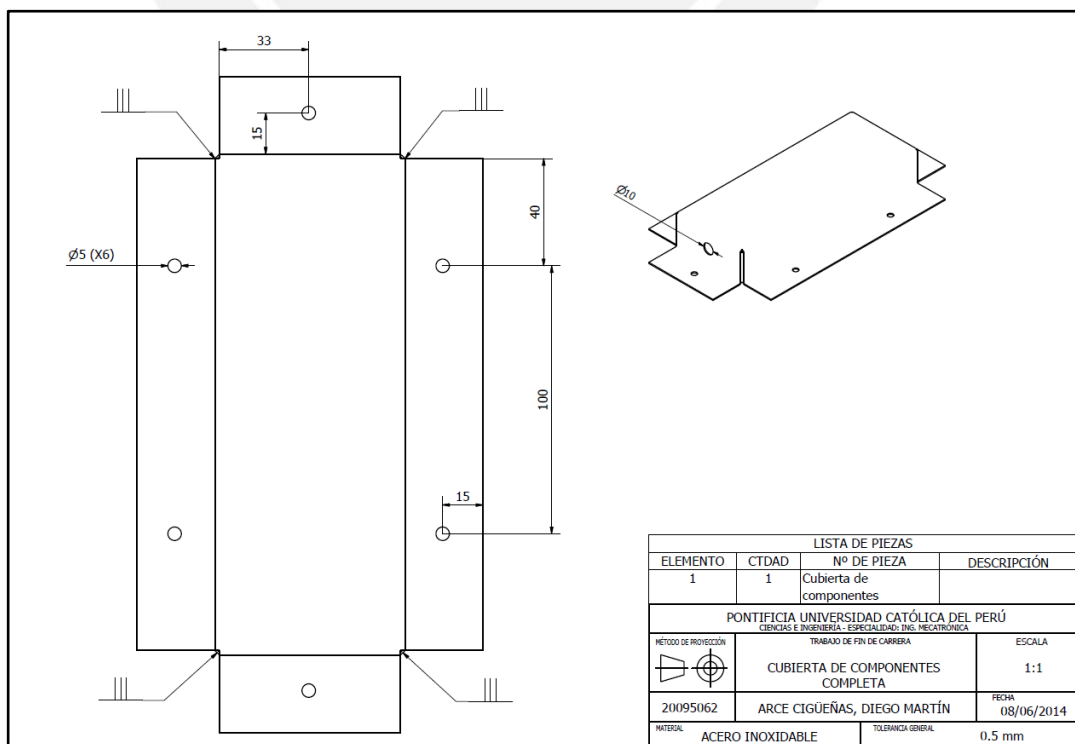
Plano de ensamblaje *Cubierta de componentes completa*.
